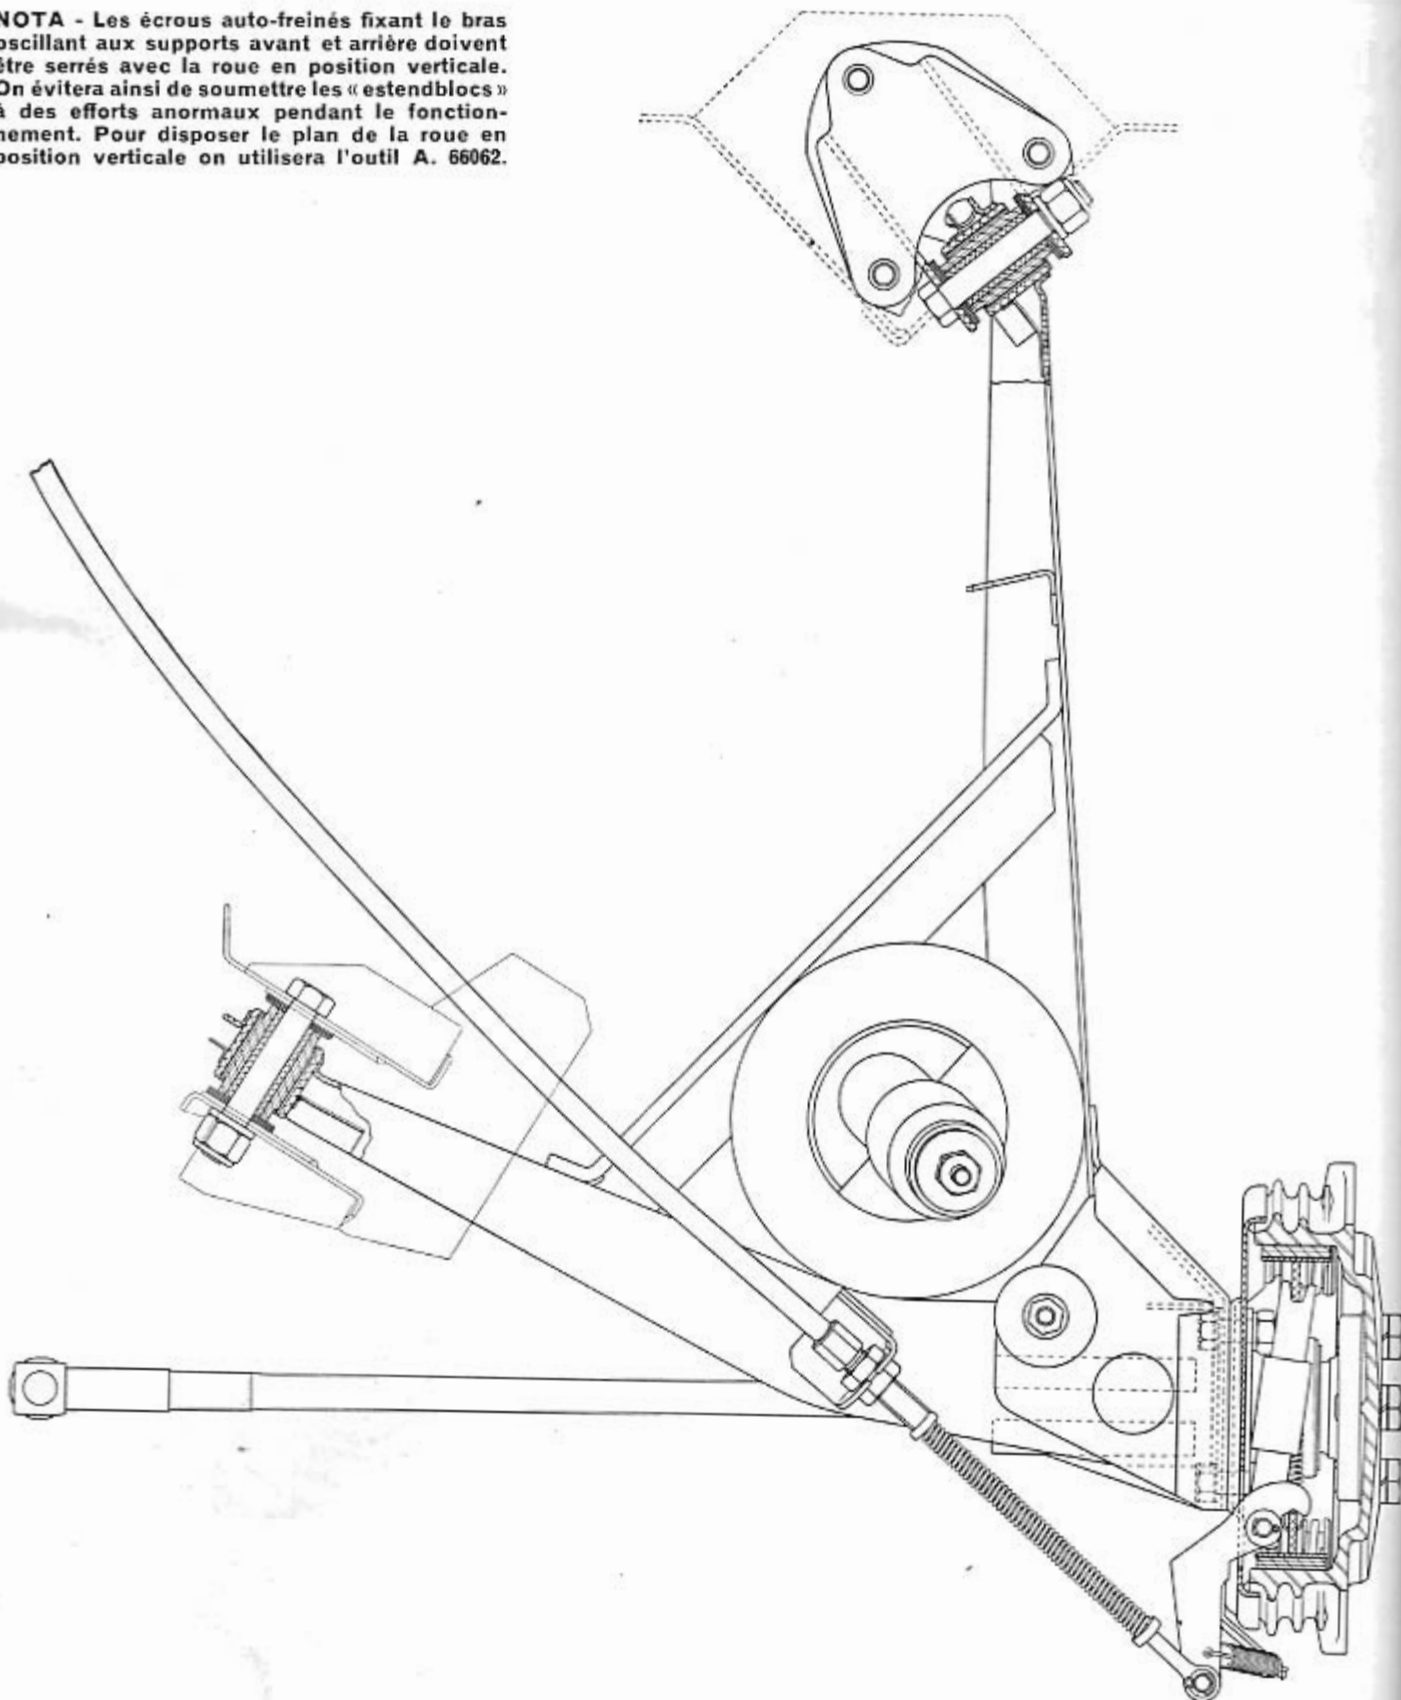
Ensemble suspension arrière droite, coupé sur le tambour de frein et sur les attaches du bras oscillant.
